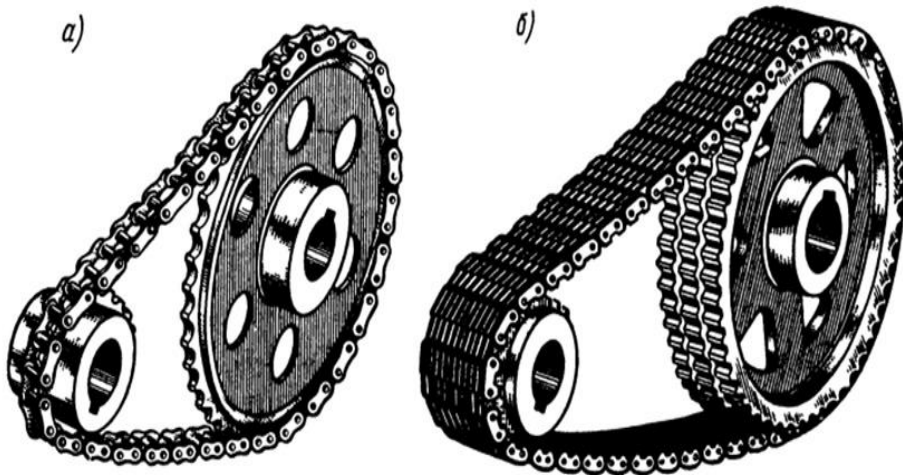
Цепная передача: *a* — роликовой цепью; *б* — зубчатой цепью
